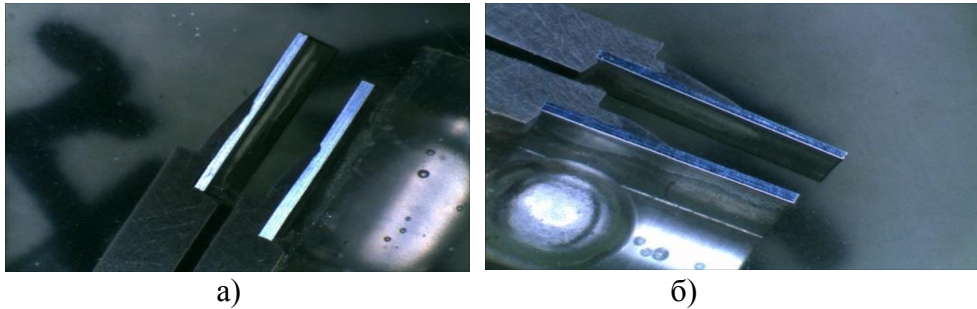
Шлифы образцов, сваренных на: а) ЭЛУ-5, б) EVOBEAM – 400
